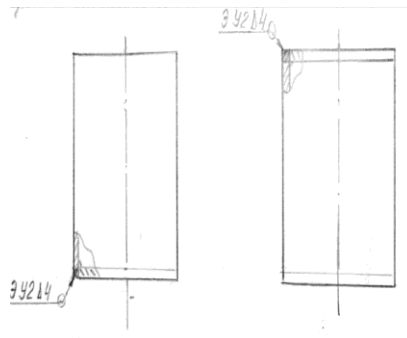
Эскиз сварки дна и стенки корпуса, потолка и стенки
